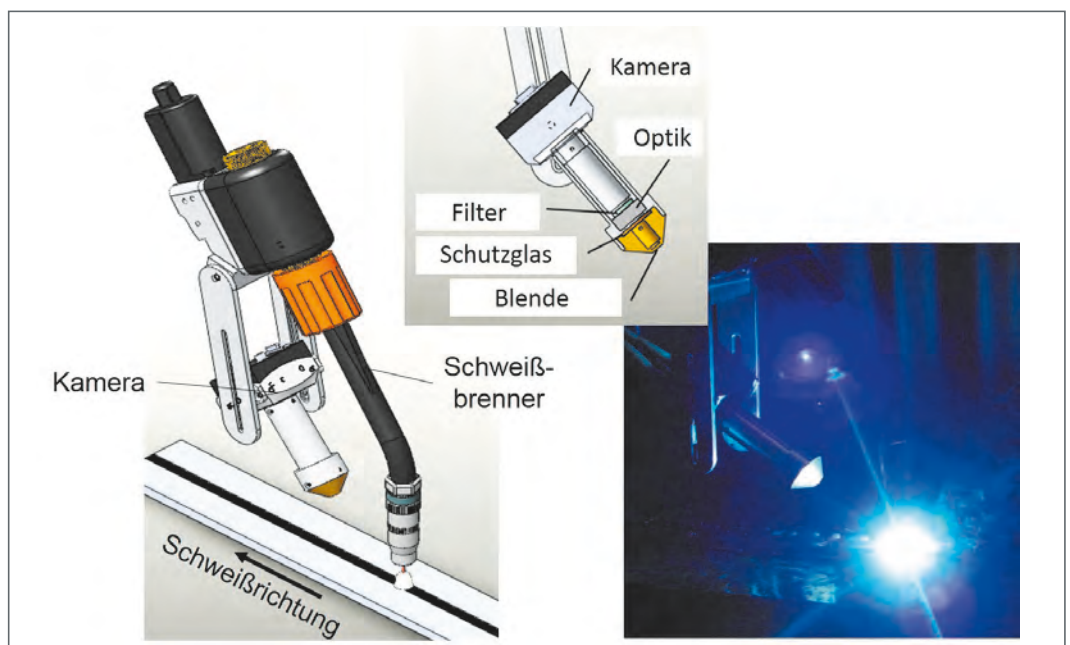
Links: Anordnung der Kamera am Schweißbrenner, Mitte: Aufbau der Kamera, Rechts: Kamera beim Schweißen
